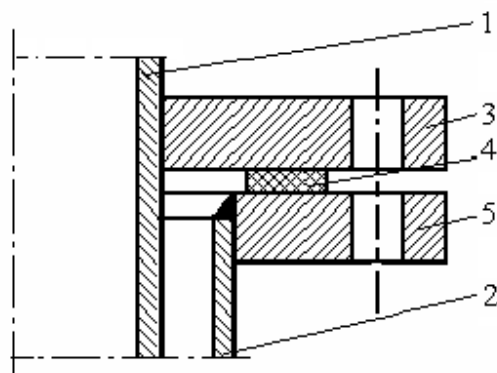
Конструкция разъемного крепления рубашки к корпусу аппарата:
